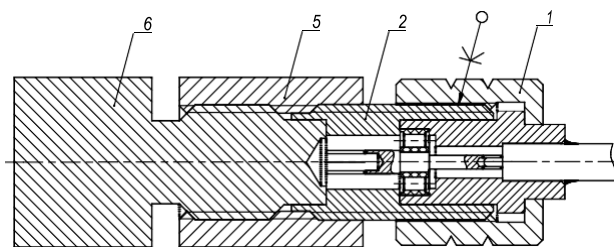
Монтаж соединителя с использованием приспособления ЖНКЮ.296371.030-02
